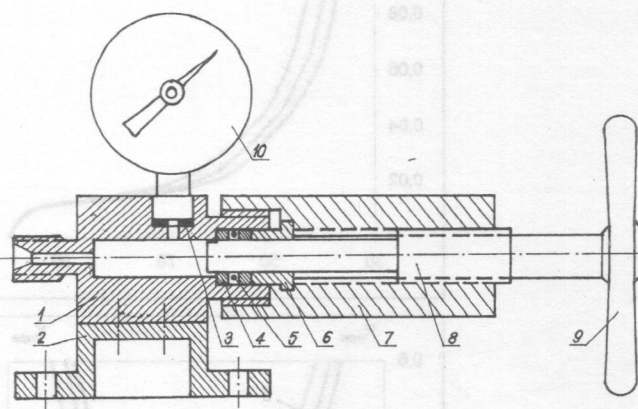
Источник жидкостного давления: 1 — корпус; 2 — подставка; 3 — медная шайба; 4 — латунные шайбы; 5 — резиновое кольцо; 6 — нажимная втулка; 7 — нажимная гайка с внутренней резьбой; 8 — шток; 9 — рукоятка; 10 — манометр
